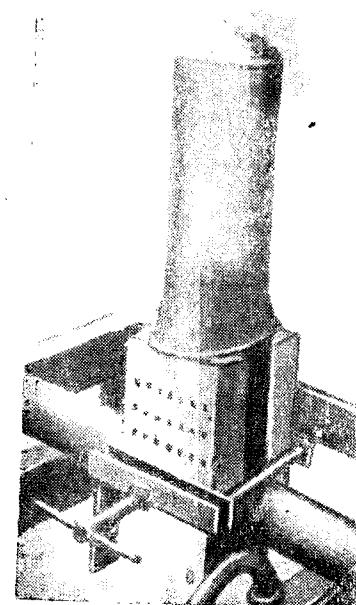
Стык, подготовленный под термитную сварку.
